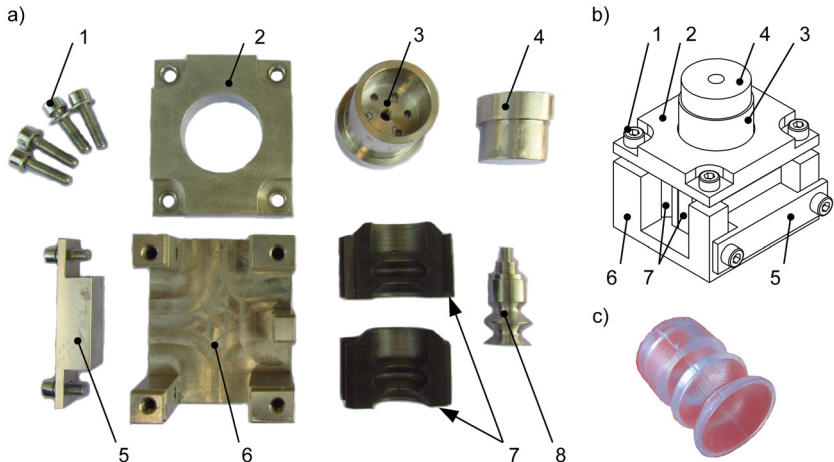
a) Einzelteile des Formwerkzeuges: (1) Innensechskantschrauben, (2) Deckel, (3) Formwerkzeugeinsatz mit Reservoir, (4) Stempel, (5) Fixierblock, (6) Rahmen, (7) Formwerkzeugeinsätze (Außenkontur des Sauggreifers), (8) Formkern (Innenkontur des Sauggreifers); b) Isometrische Ansicht des zusammengebauten Formwerkzeuges; c) entformtes Funktionsmuster
